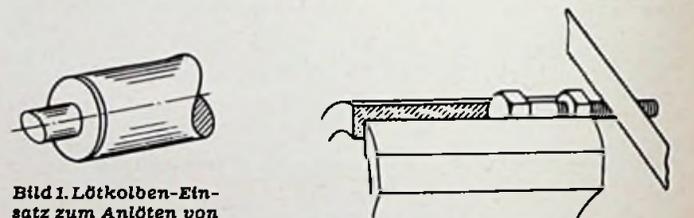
LötKolben-Einsatz zum Anlöten von Verbindungen am Chassisblech
